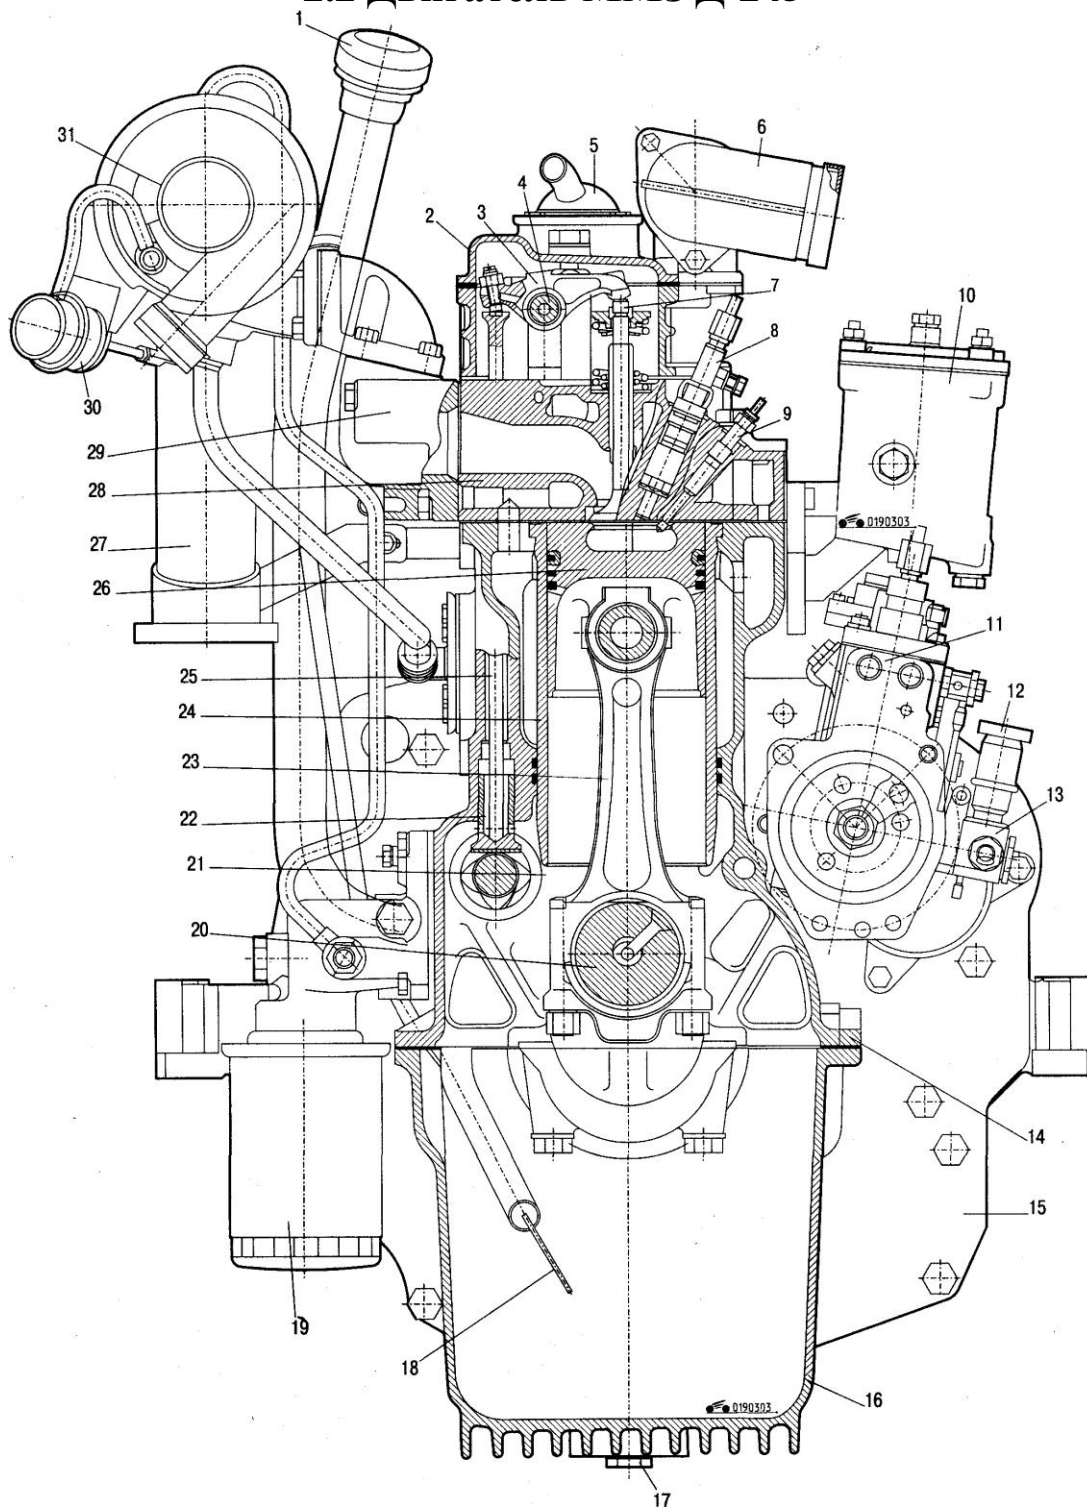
Поперечный разрез дизелей Д-245.30Е2С и Д-245.9Е2: 1 - маслоналивная горловина; 2 - колпак; 3 - коромысло; 4 - ось коромысел; 5 - клапан вентиляции картера; 6 - воздухопровод; 7 - клапан; 8 - форсунка; 9 - свеча накаливания; 10 - фильтр тонкой очистки топлива; 11 - топливный насос высокого давления; 12 - топливопрокачивающий насос; 13 - топливоподкачивающий насос; 14 - блок цилиндров; 15 - задний лист; 16 - масляный картер; 17 - маслосливная пробка; 18 - указатель уровня масла; 19 - масляный фильтр; 20 - коленчатый вал; 21 - распределительный вал; 22 - толкатель; 23 - шатун; 24 - гильза блока цилиндров; 25 - штанга толкателя; 26 - поршень; 27 - выпускной газопровод; 28 - головка цилиндров; 29 - выпускной коллектор; 30 - перепускной клапан турбокомпрессора; 31 - турбокомпрессор
